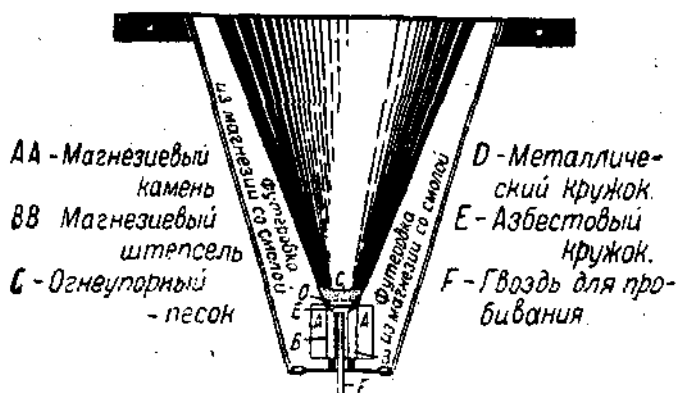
Вертикальный разрез автоматического тигля для термитной сварки с показанием заделки выпускного отверстия.
